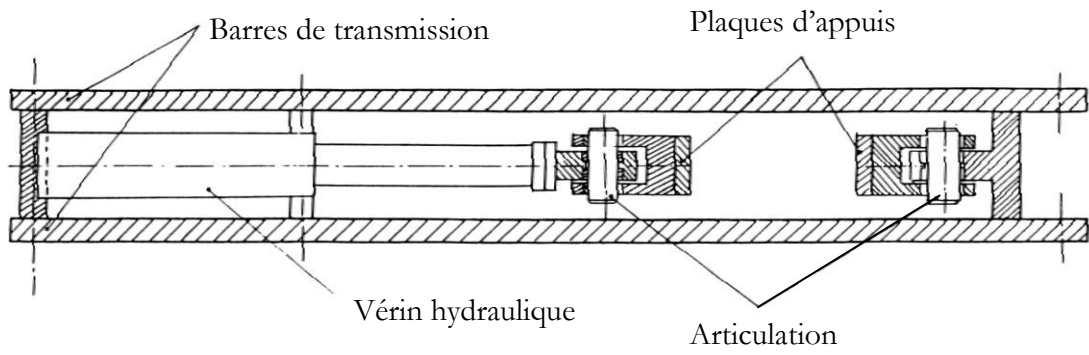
Vue d'ensemble de la presse uniaxiale
